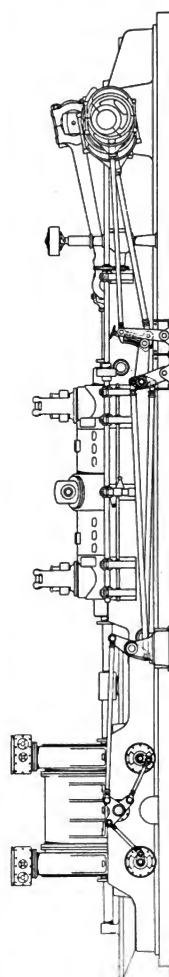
Disposition der Gebläse-Ansaugsteuerung der Siegerner Maschinenbau-Akt.-Ges. in Siegen (D. R. P.).
